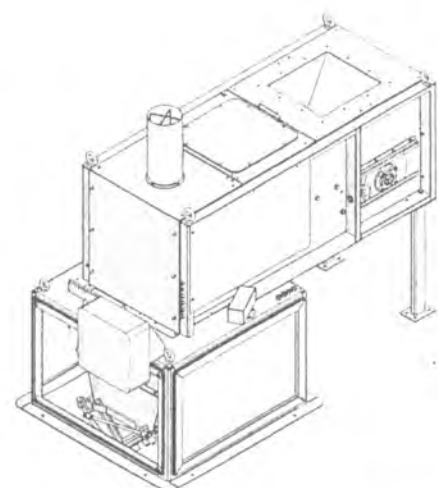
Внешний вид весов с защитным кожухом и ленточным питателем
